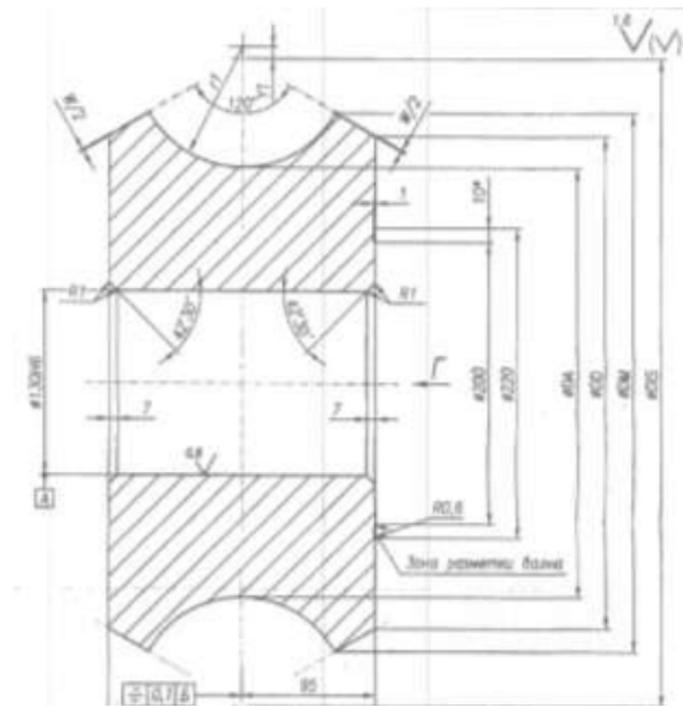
Общий вид отливки «Трубопрокатный валок» из чугуна ТШХН-50 [1]
